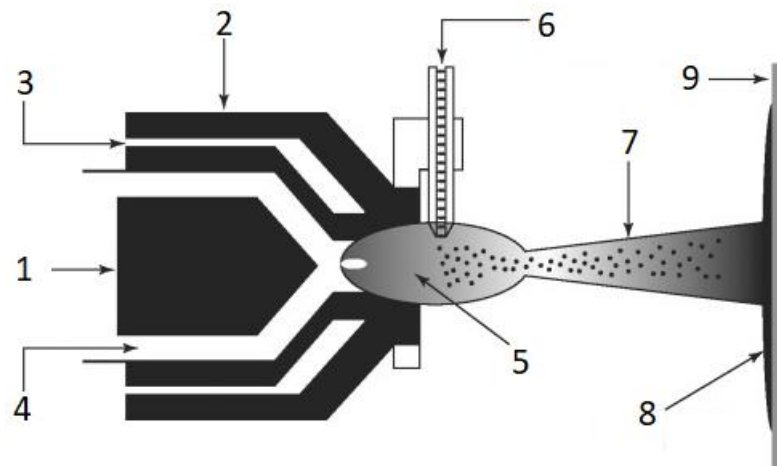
Принципова схема техніки плазмового напилення для формування покриттів [17]: 1 – катод плазмотрона; 2 – анод плазмотрона; 3 – водяне охолодження; 4 – плазмоутворюючий газ; 5 – плазмова дуга; 6 – подача порошку; 7 – плазмовий струмінь; 8 – напилене покриття; 9 – металева підкладка (основа).
